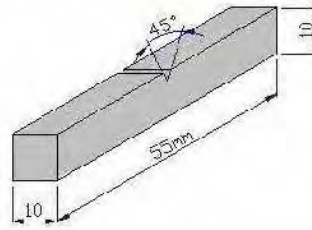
Corpo de Prova Padrão Charpy com entalhe.
